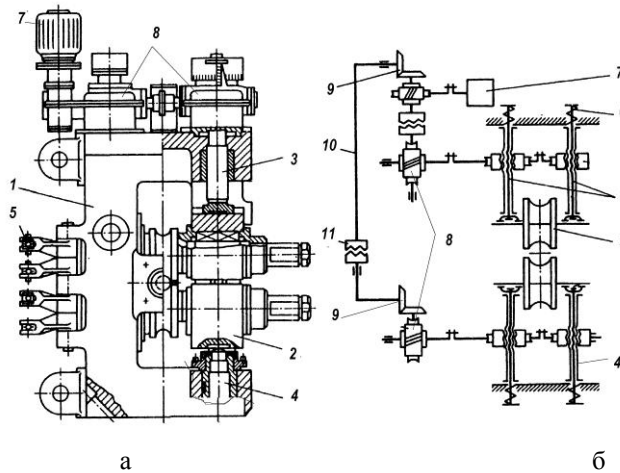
Загальний вигляд (а) та кінематична схема (б) робочої кліть безперервного розкатного стану
